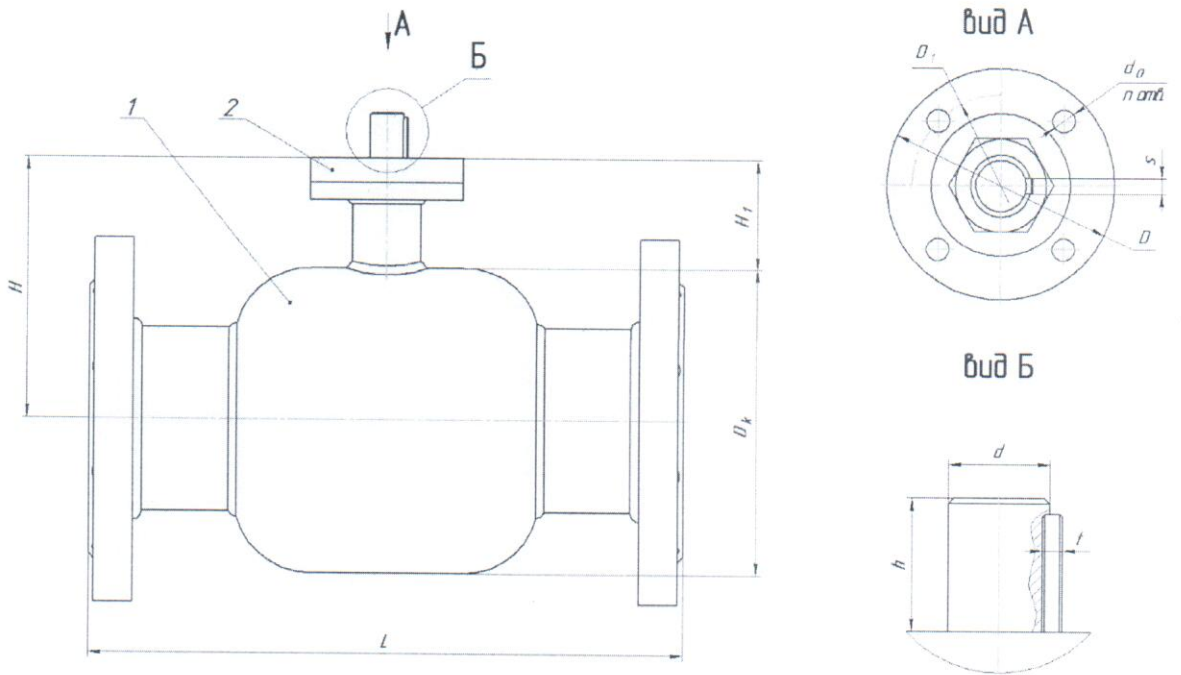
Кран шаровой цельносварной фланцевый под привод
